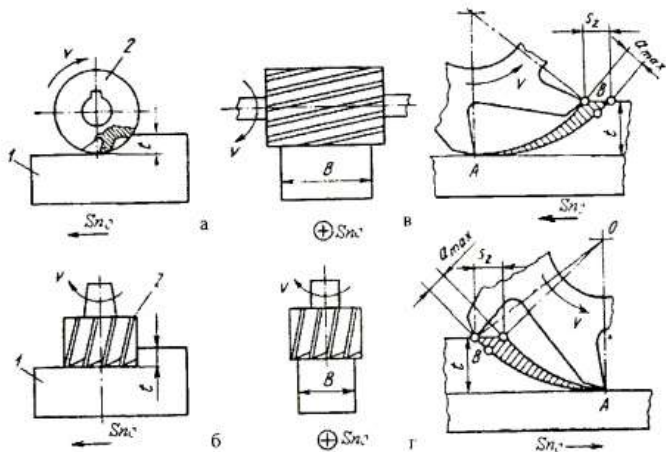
Схеми фрезерування циліндричною і торцевою фрезами
